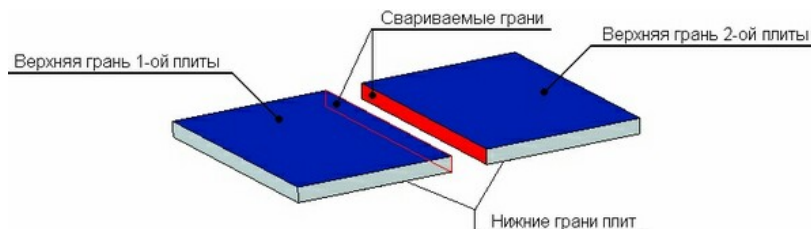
Выбор граней при создании стыкового сварного шва
